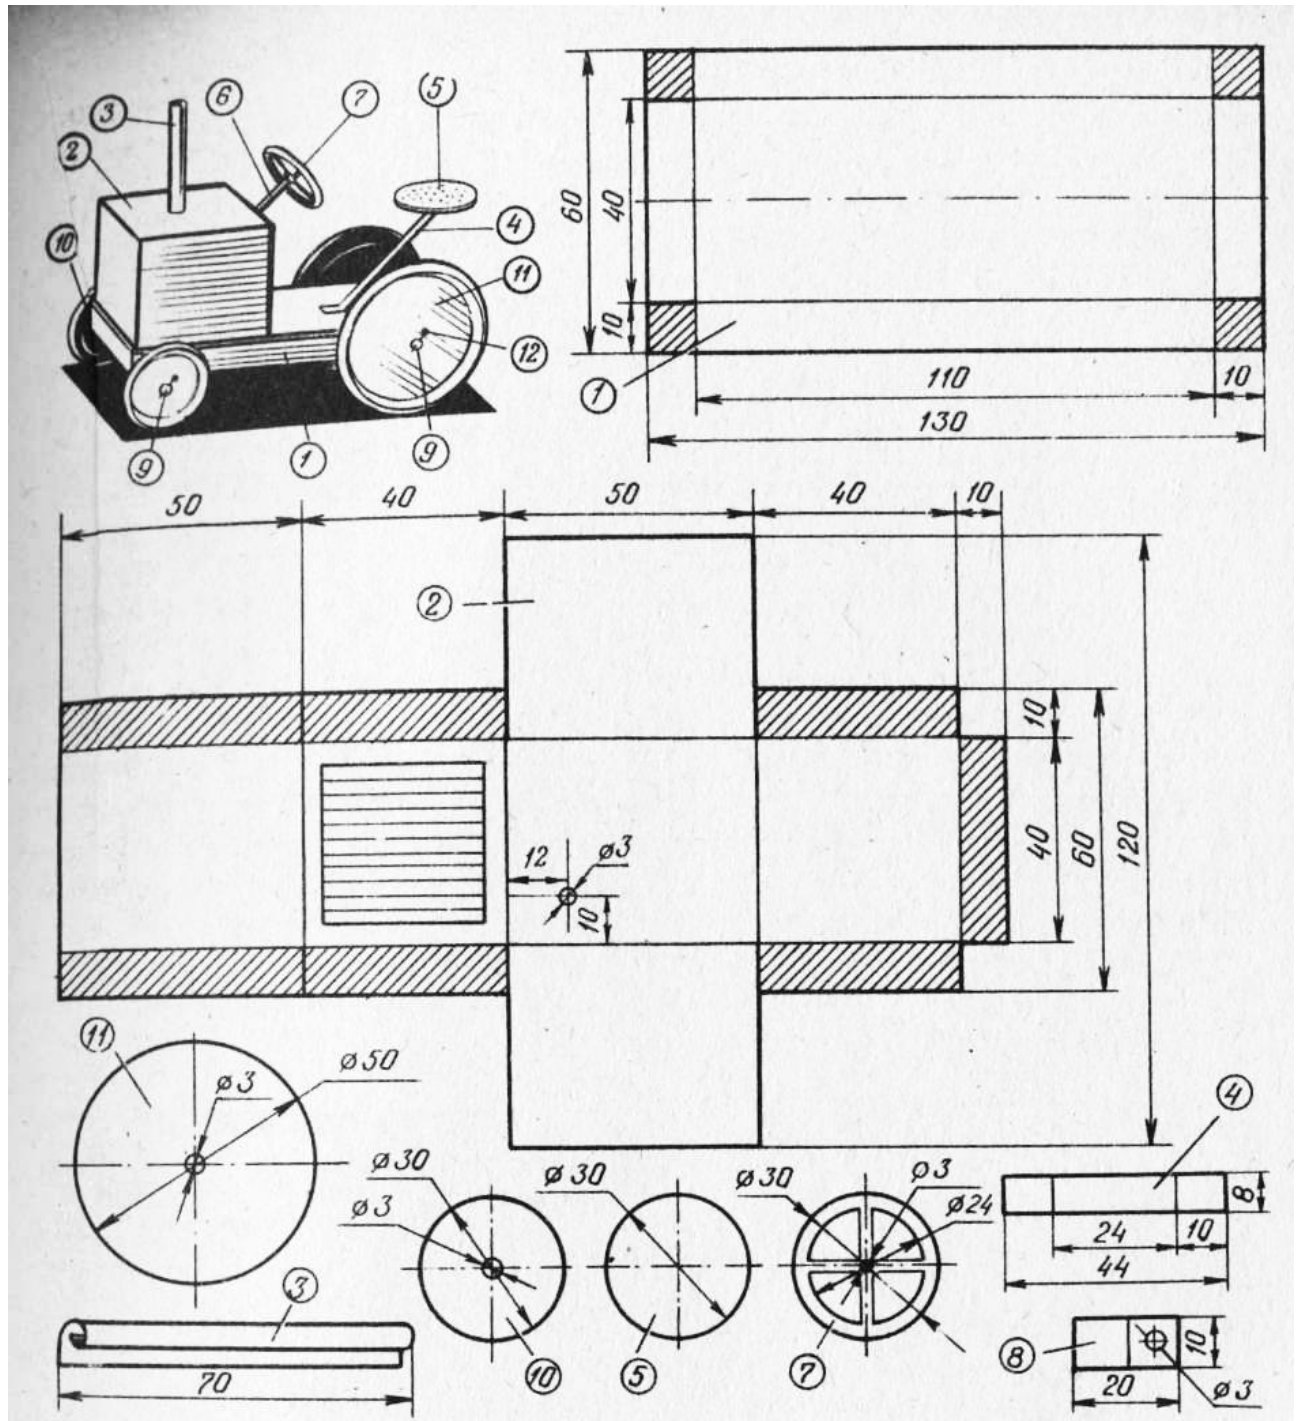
Модель трактора для обработки пришкольного участка: 1— рама; 2— капот; 3 — выхлопная труба; 4 — подставка для сиденья; 5 — сиденье; 6 — колонка руля; 7 — рулевое колесо; 8 — подшипник; 9 — ось; 10 — переднее колесо; 11 — заднее колесо; 12— шплинт
